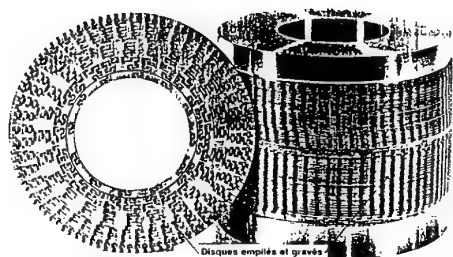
Disques de laminage de la vanne silencieuse "Control Component"
